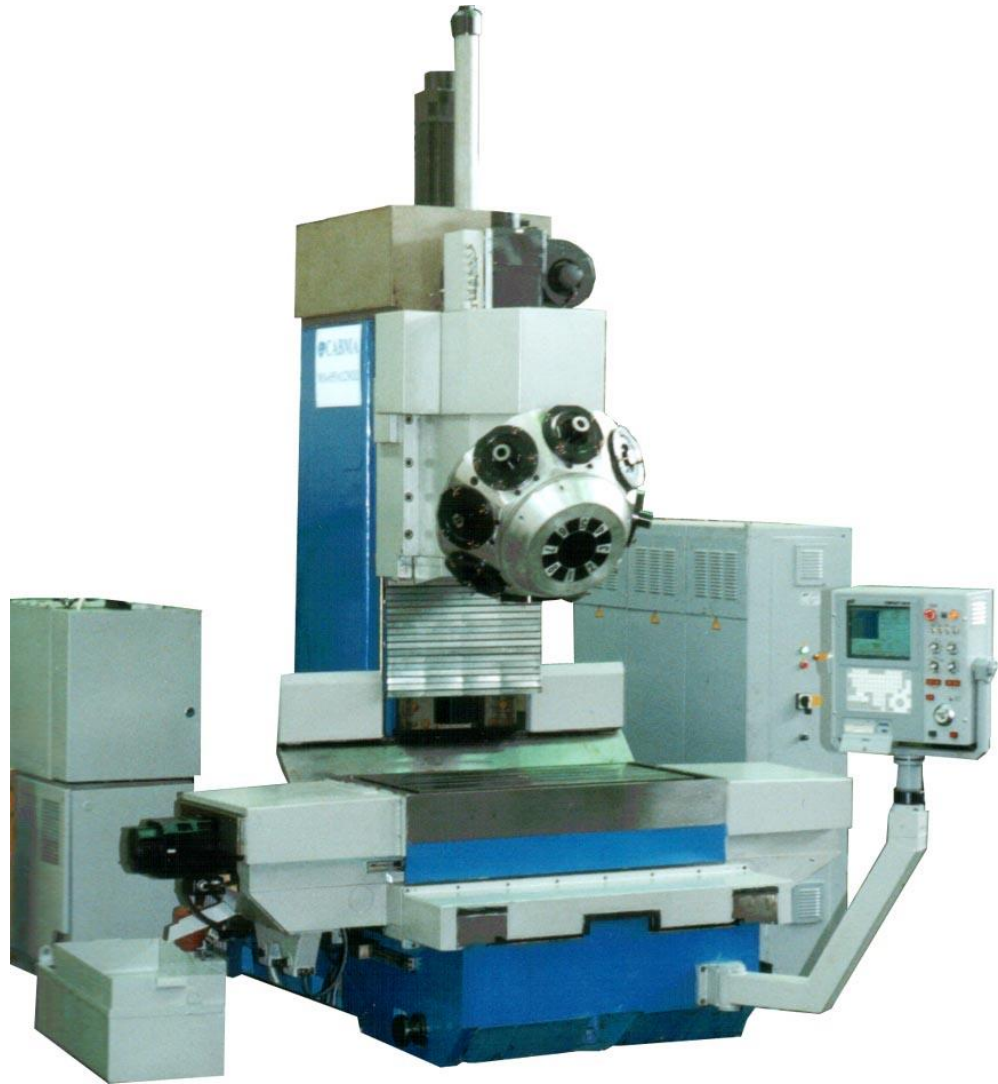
Загальний вигляд вертикального фрезерного верстата MA655A7
